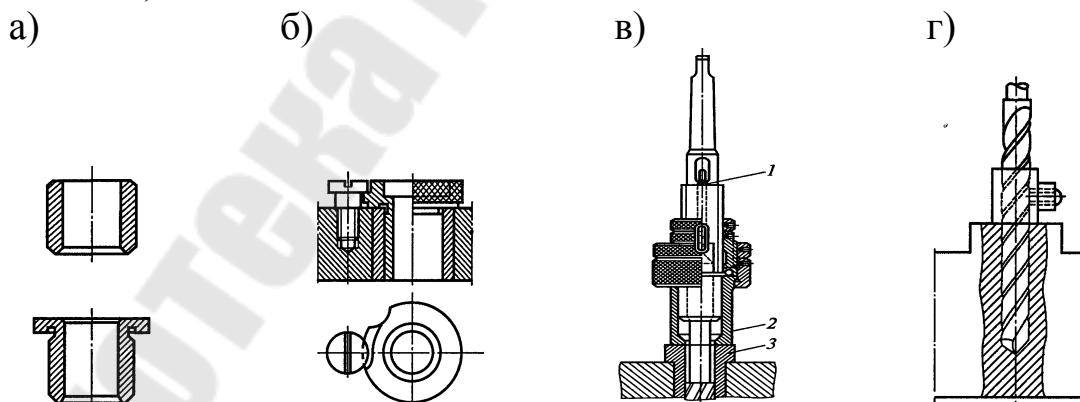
Кондукторные втулки (а – постоянные; б - быстросменные) и приспособления для ограничения движения подачи шпинделя (в – патрон с регулируемым упором; г – упорное кольцо)
